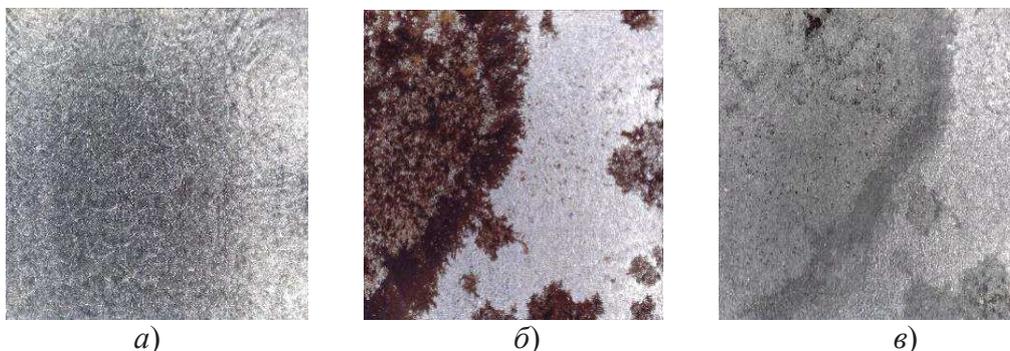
Внешний вид стальных поверхностей после подготовки различными способами: а) способ 1 и 2, б) способ 3, в) способ 4
